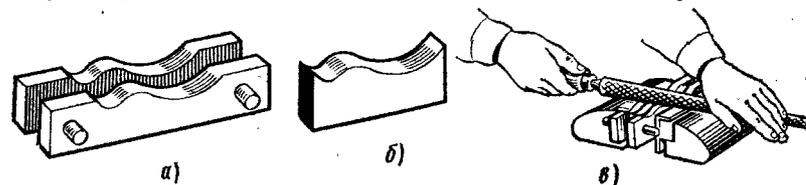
Опилкивание в копируальном приспособлении: а — приспособление; б — образец детали; в — прием работы
